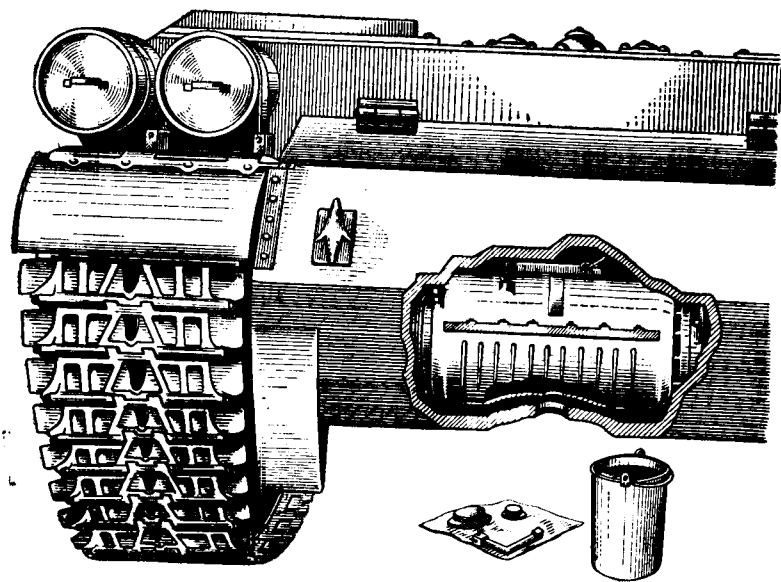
Отверстия для слива масла из картера механизма передач и поворотов
